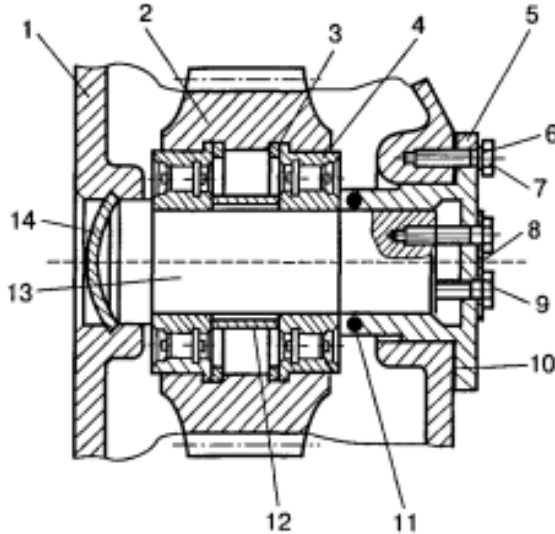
Збиральна одиниця для завдання № 4: 1 – корпус; 2 – колесо зубчасте; 3 – кільце (2 шт.); 4 – підшипник (2 шт.); 5 – фланець; 6 – шайба пружинна (6 шт.); 7 – болт (6 шт.); 8 – планка стопорна; 9 – болт (3 шт.); 10 – прокладка; 11, 12 – ущільнення; 13 – вал; 14 – кришка
